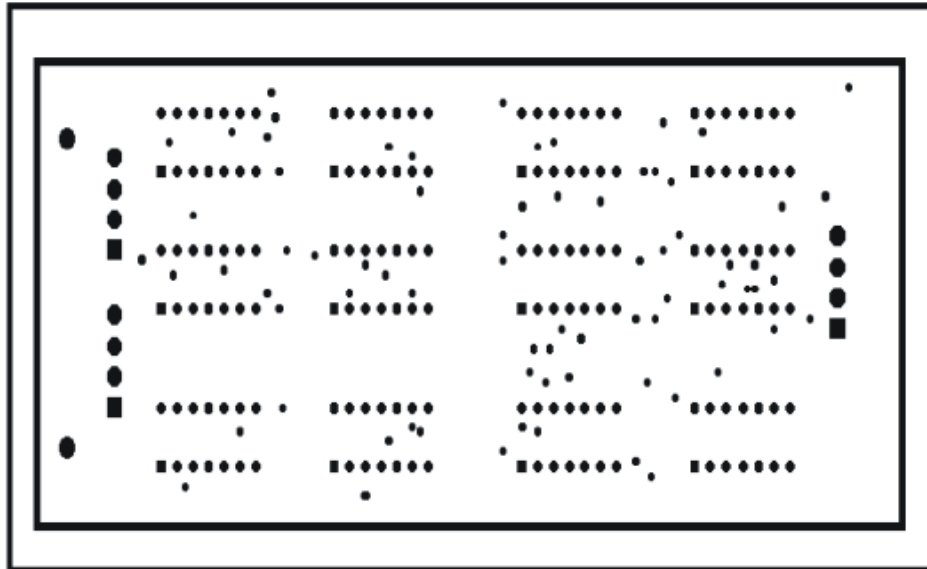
Cara de la reserva de soldadura[40]
